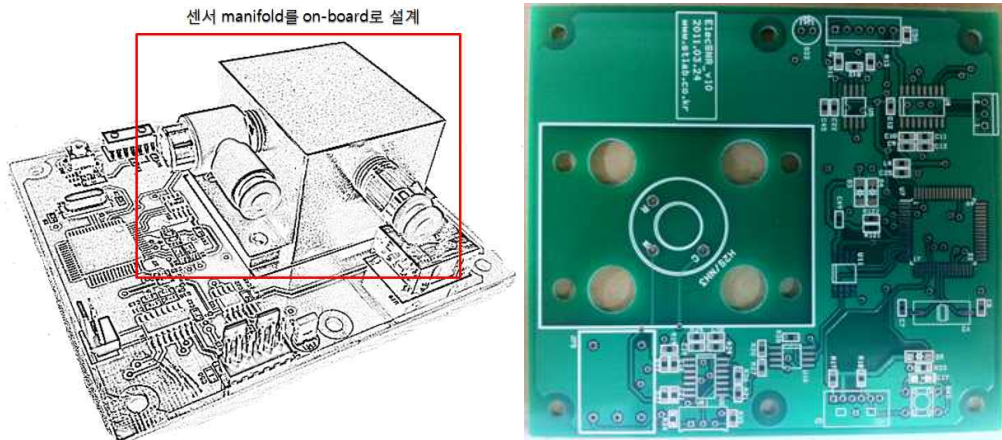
On-board형태로 센서 manifold를 PCB에 고정(제작 예제)
